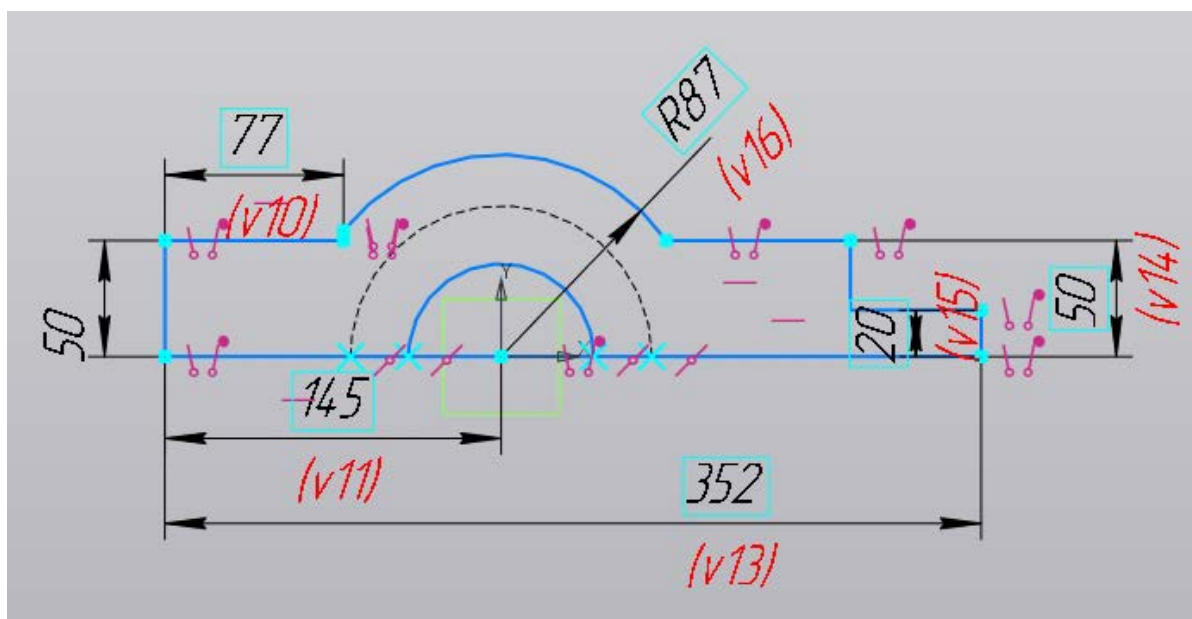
Эскиз опоры сварного корпуса
